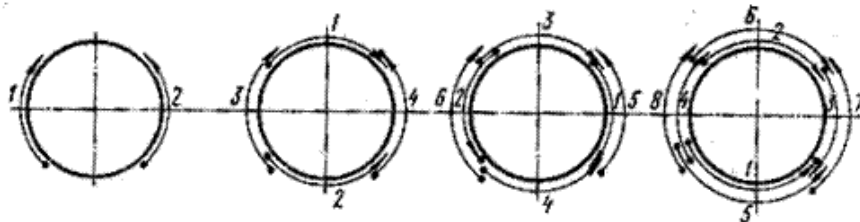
Схема сварки стыка трубы: а – второго слоя, б – третьего слоя
